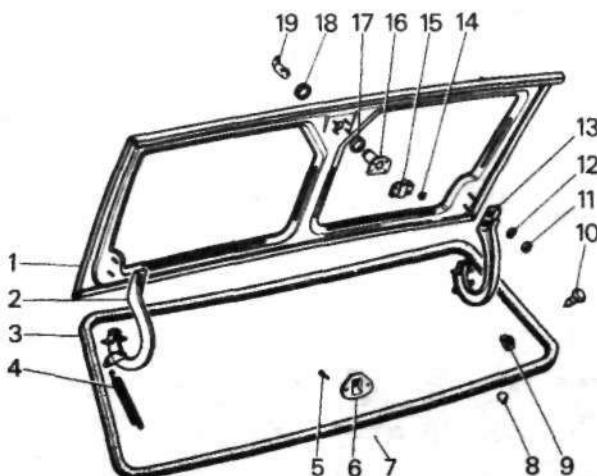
Расположение деталей крышки багажника (Раздел 19)
